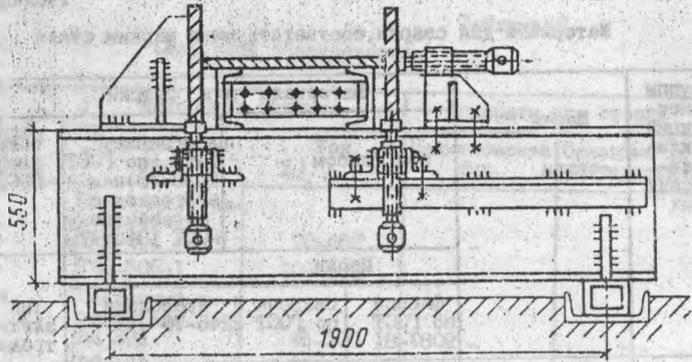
Кондуктор с винтовыми прижимами для сборки сварных двутавров.
